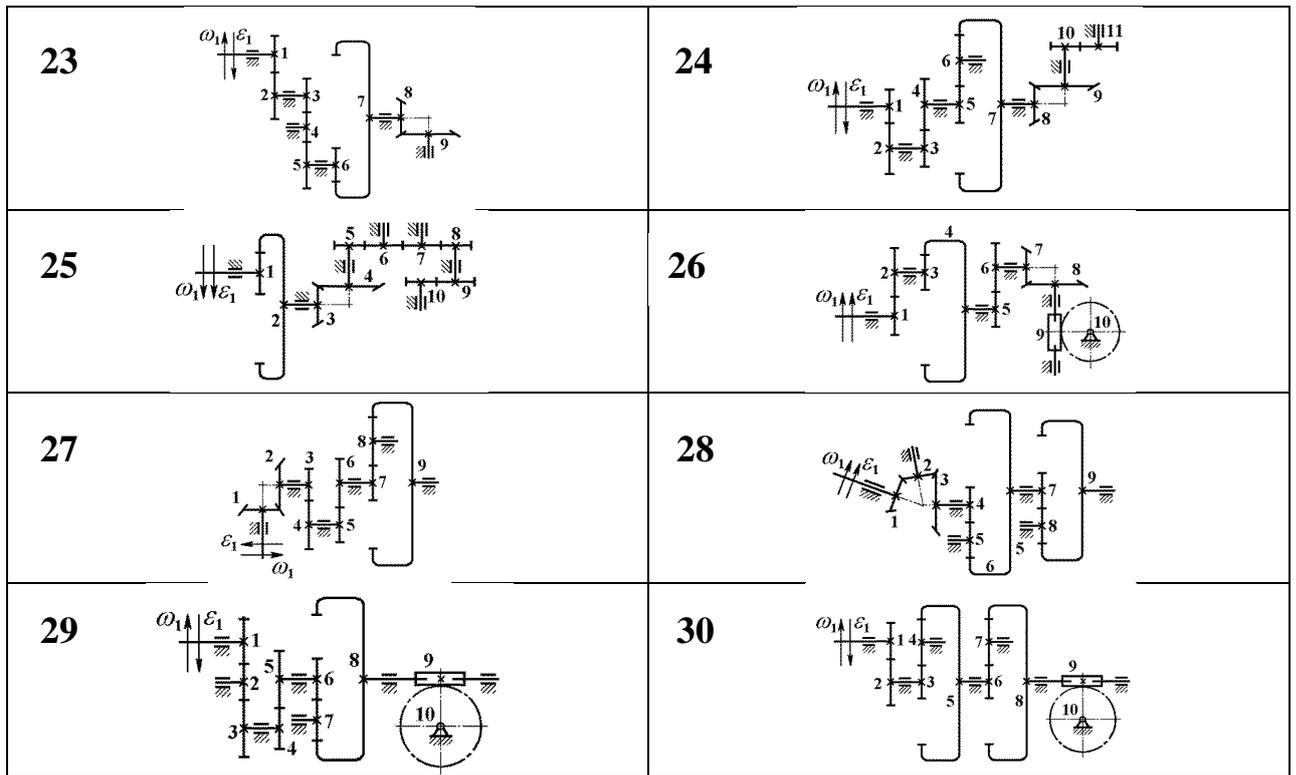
Схемы зубчатых механизмов с неподвижными осями колес
